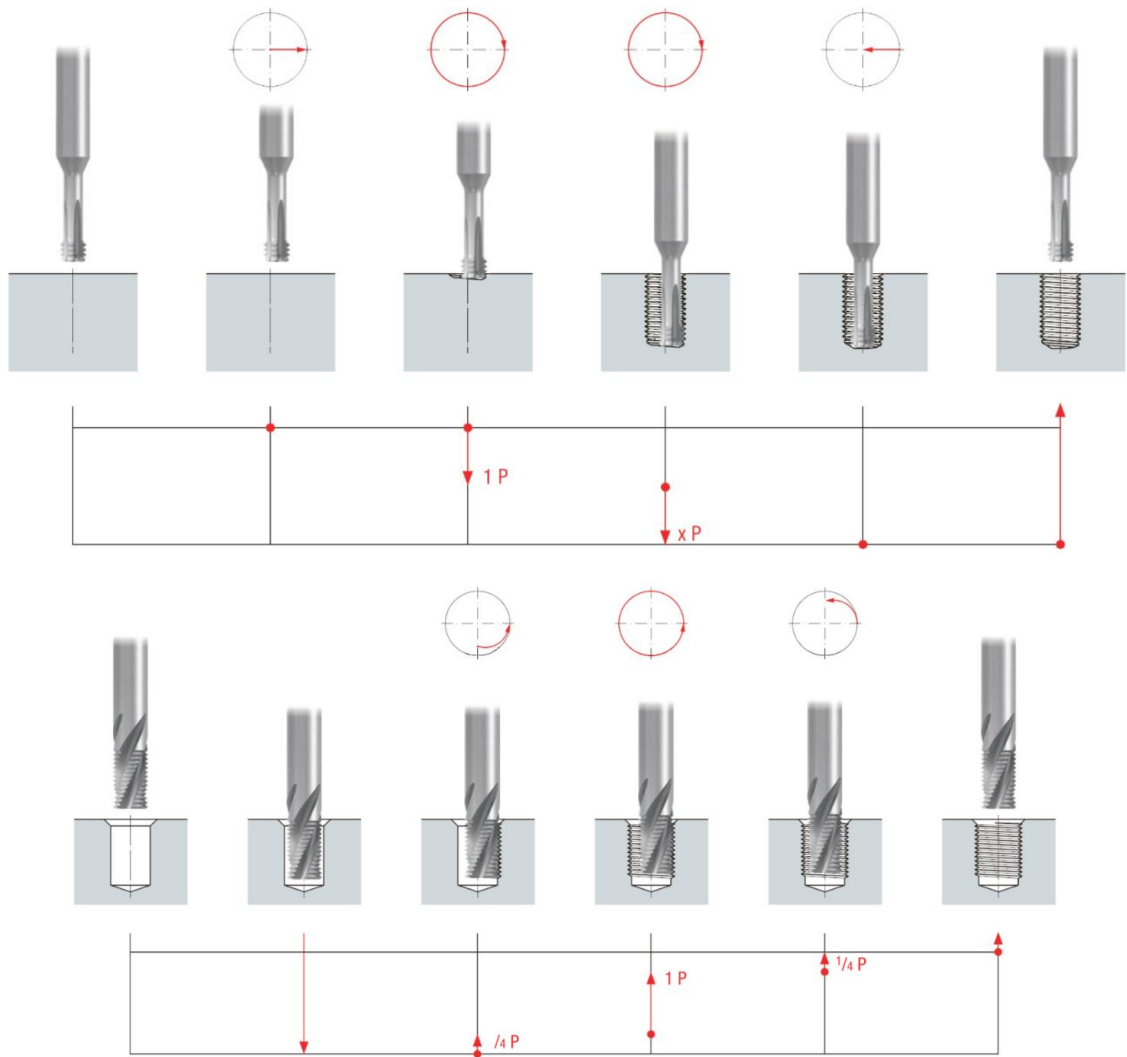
Схеми врізання різьбової фрези у заготовку [22]
